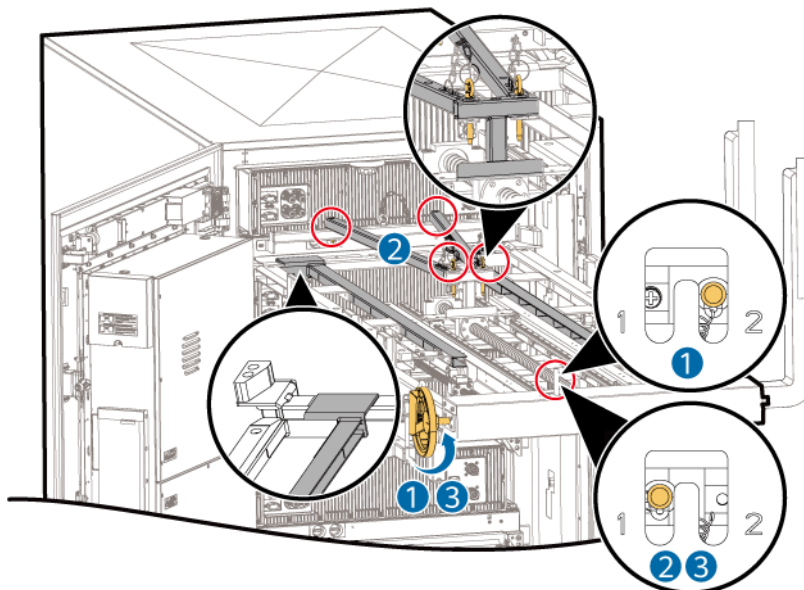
Installazione del dispositivo di fissaggio del gruppo
